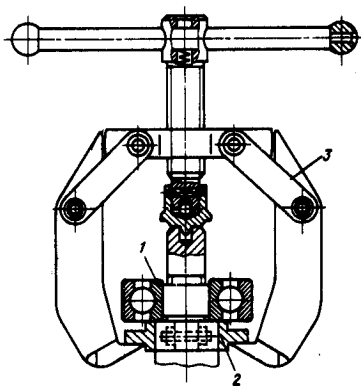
Демонтаж шарикоподшипника с вала с использованием разъемного кольца
